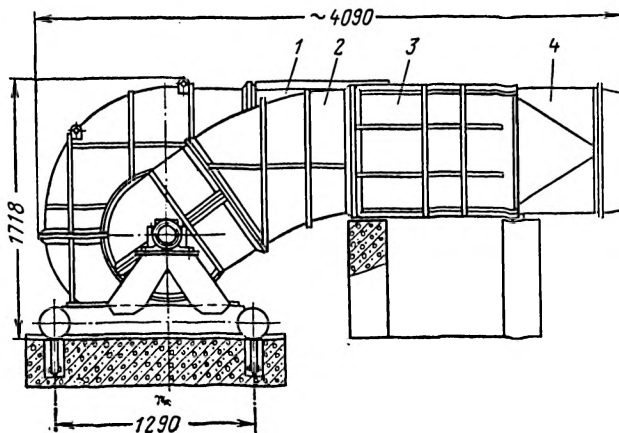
Вентилятор ВЦПД-8УМ с реверсивным устройством
